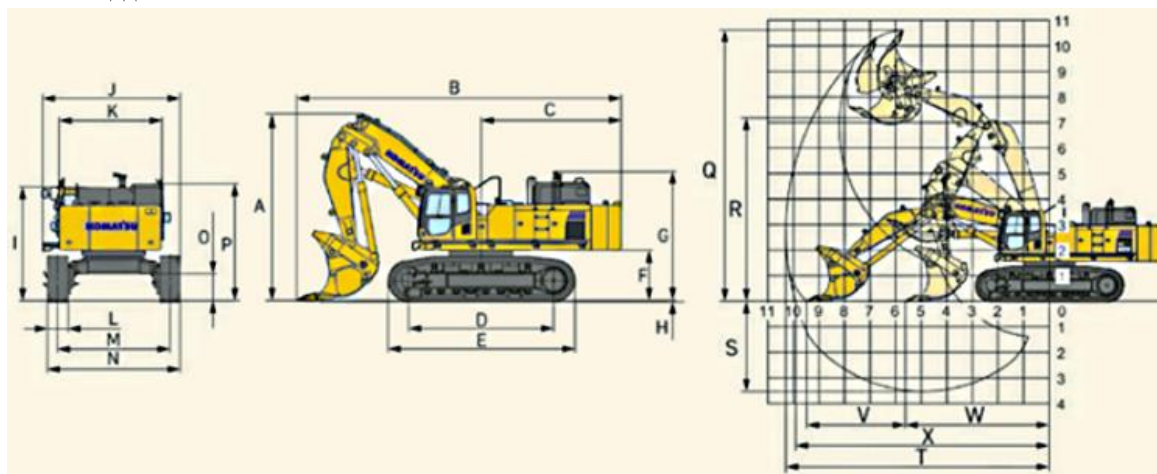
Рабочие параметры карьерного экскаватора Komatsu PC4000-11
